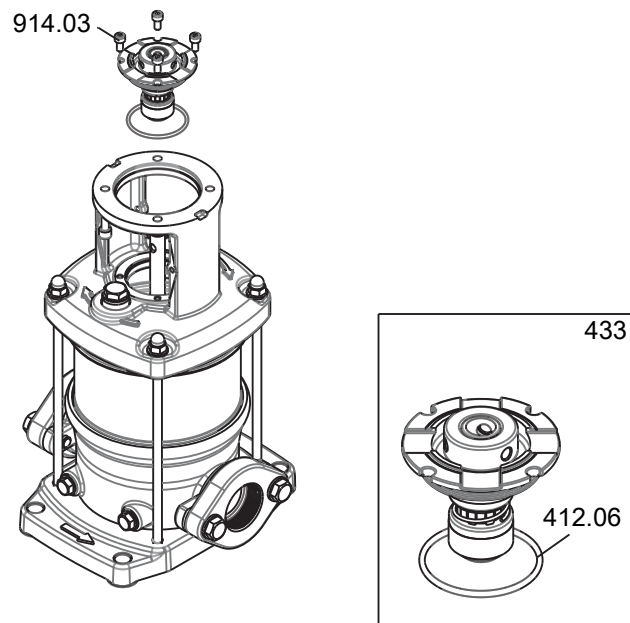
Montar o empanque mecânico (desenho de exemplo)
